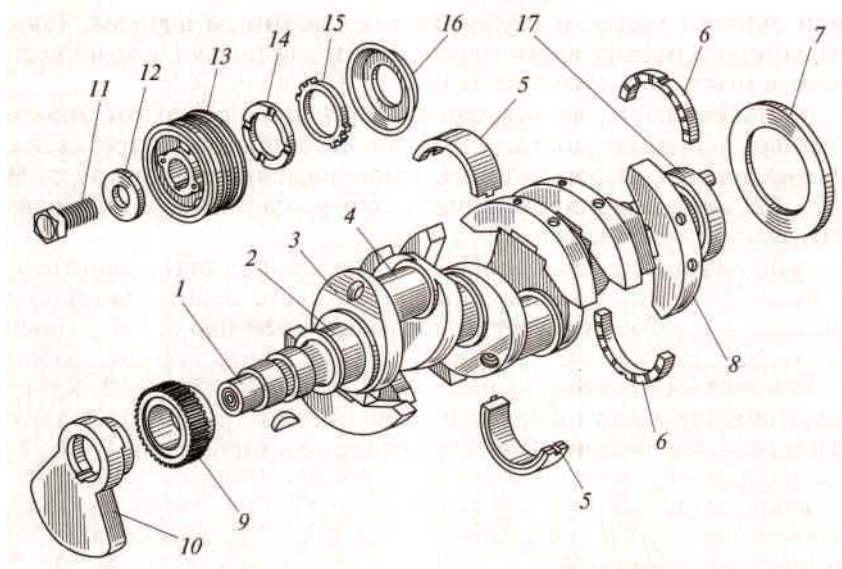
Коленчатый вал двигателя ЯМЗ-236:
